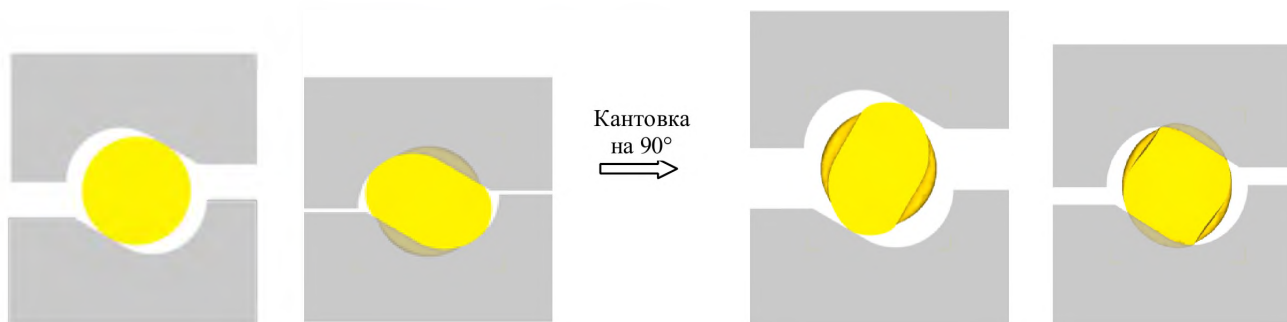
Схемаковки (протяжки) заготовок в бойках новой конструкции
